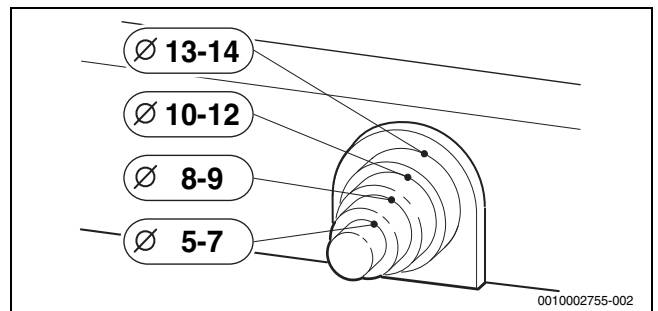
Zugentlastung an Kabeldurchmesser anpassen
